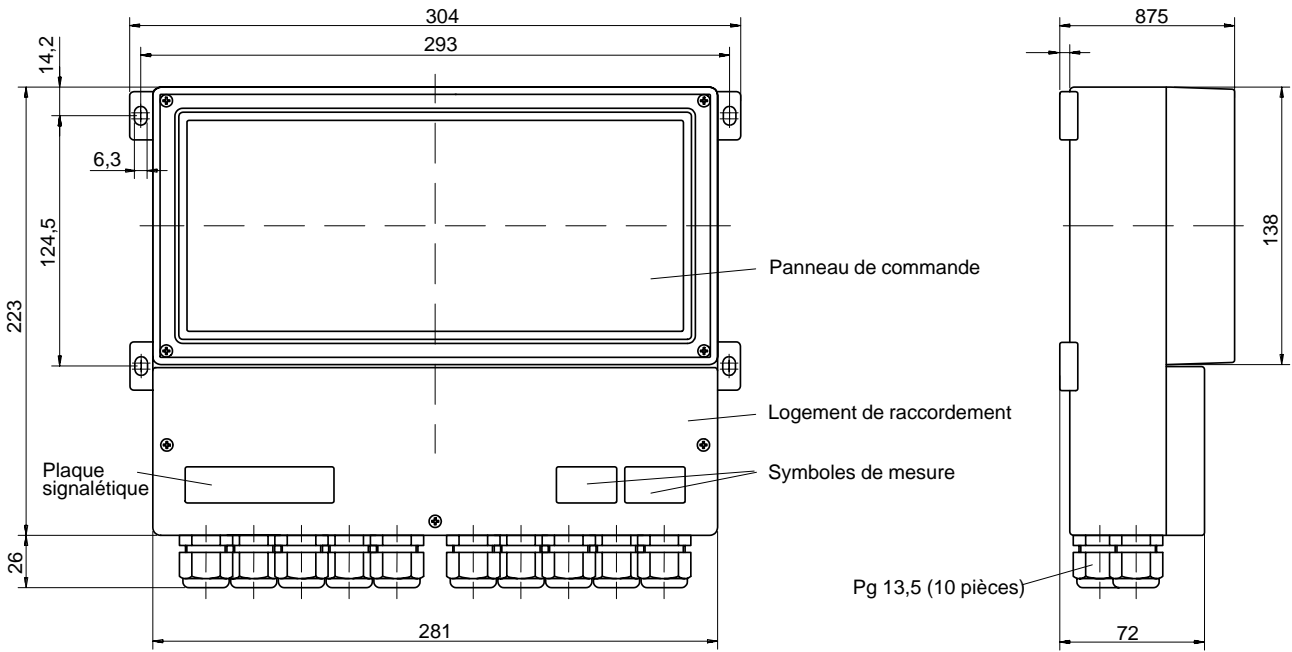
Dessin d'encombrement du Transmetteur 7500
